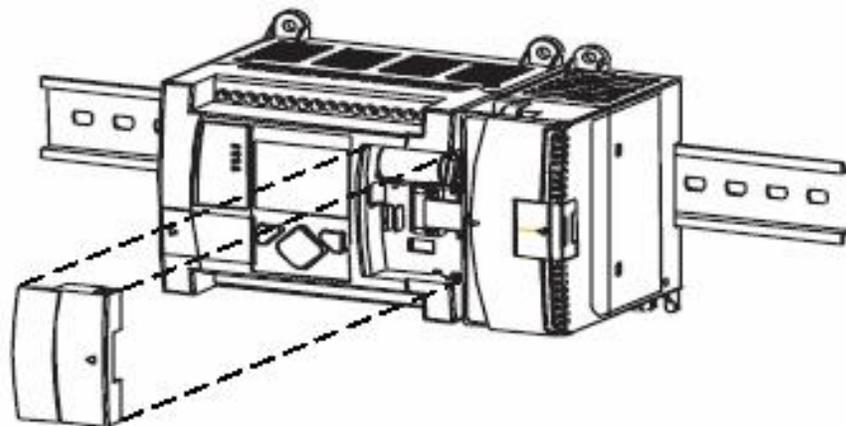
Montaje del modulo de expansión 1762-IR4
